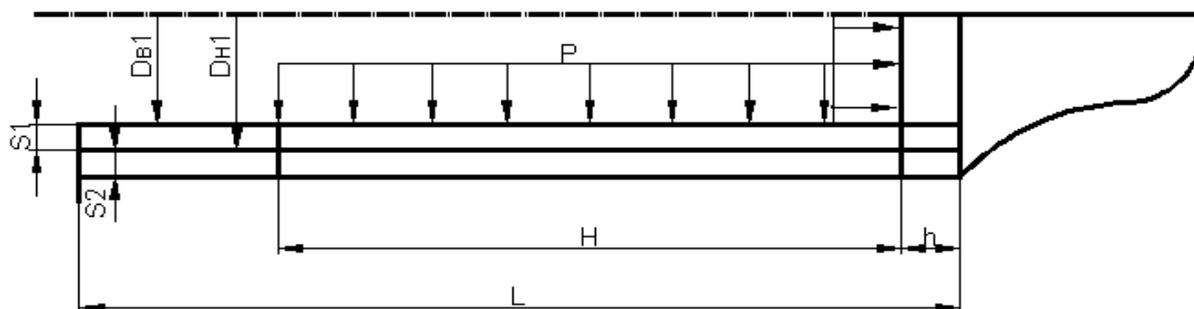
Схема плоской параметрической модели двухслойного гидроцилиндра для крепи М144
